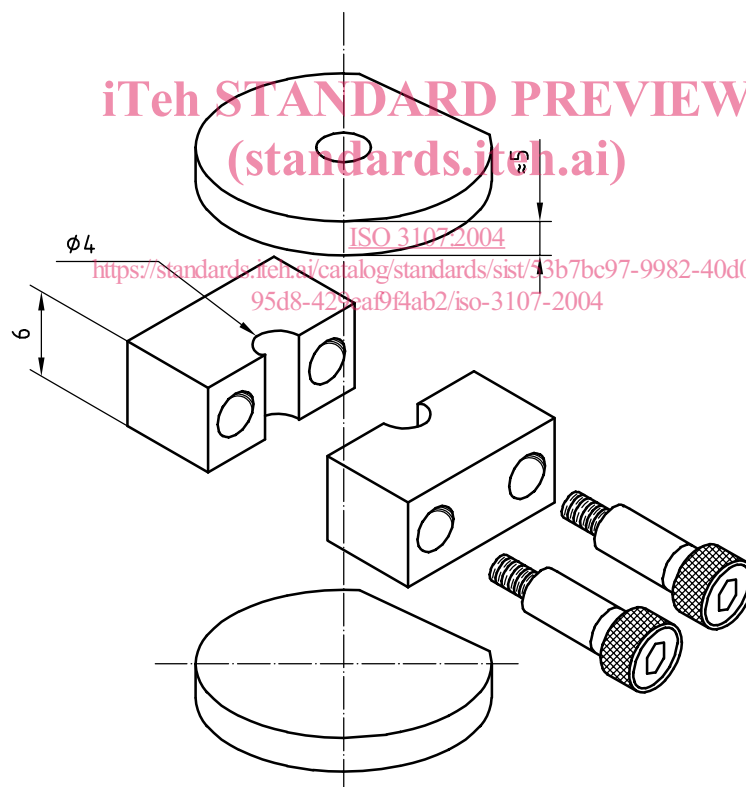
Moule pour la préparation des éprouvettes destinées à l'essai de compression
